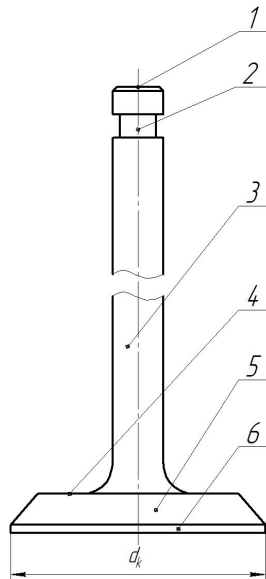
Клапан двигателя Д-243, Д-245, Д-260:
